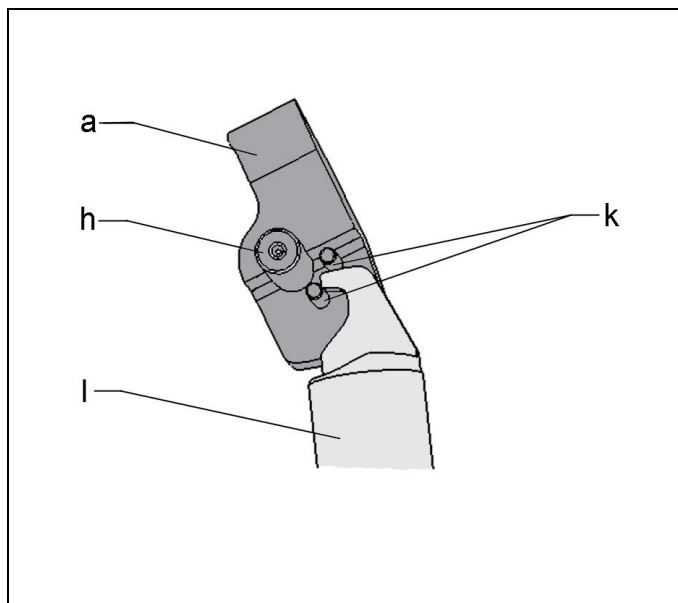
Smontaggio / montaggio della leva di bloccaggio
